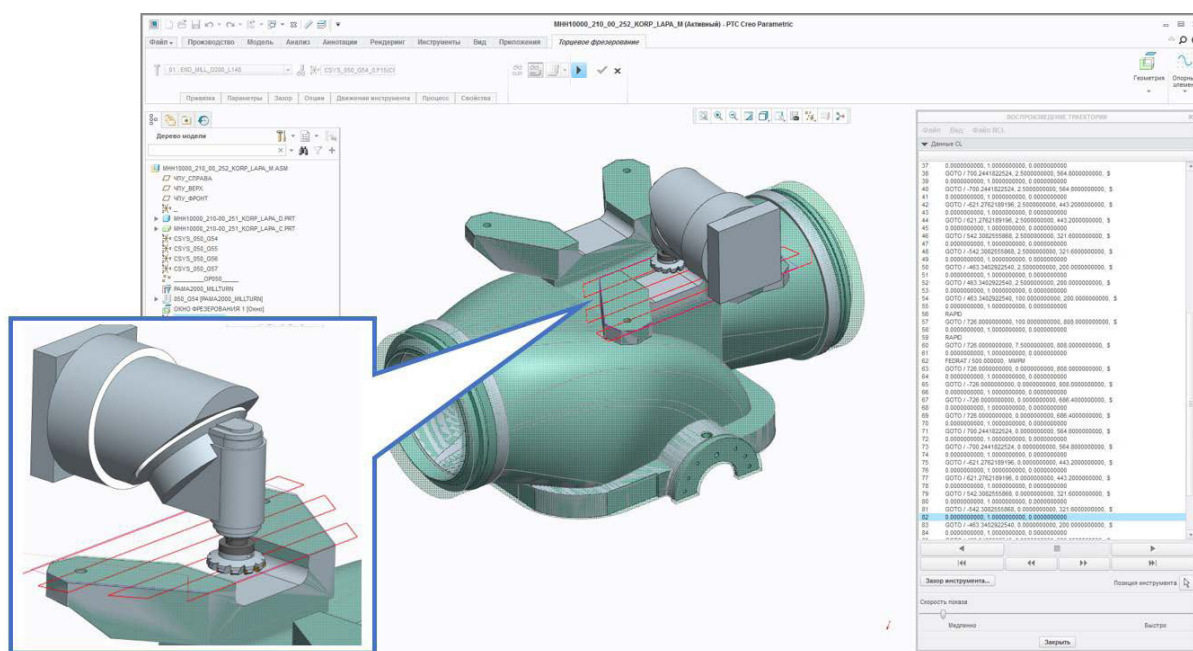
Фрезерование поверхности лап корпуса магистрального насоса в САМ-модуле Creo Parametric
